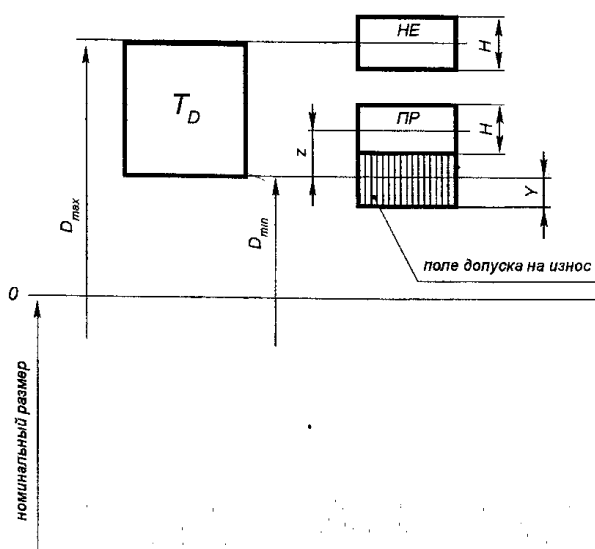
Схема расположения полей допусков калибров для контроля отверстий изготовленных по квалитетам 6, 7 и 8 при номинальных размерах до 180 мм (для размеров отверстий изготовленных по квалитетам от 9 до 17, $Y = 0$)
